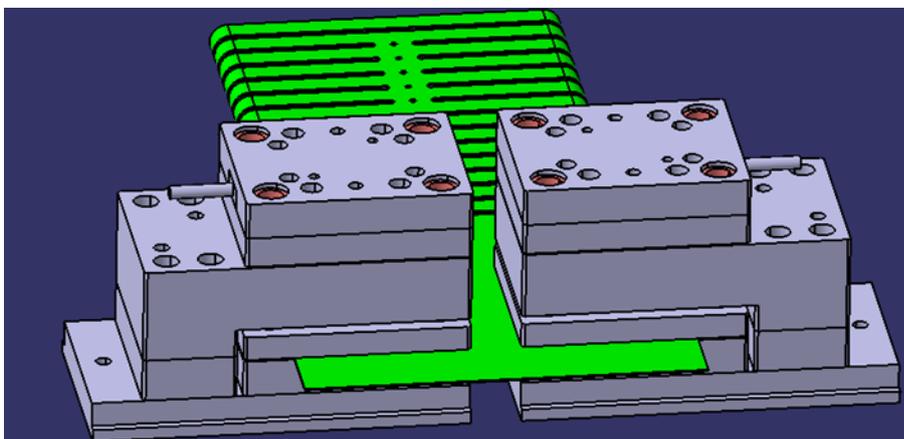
Baugruppe Abschneiden: Zusammenbau
